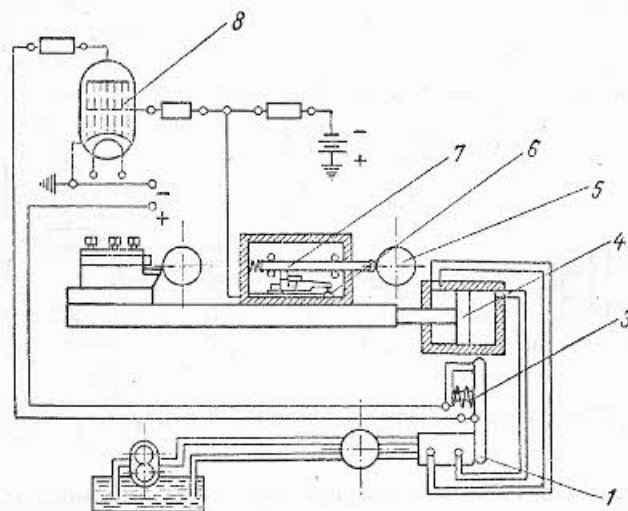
Sistem de copiere electrohidraulic adaptat la sania unui strung universal.
